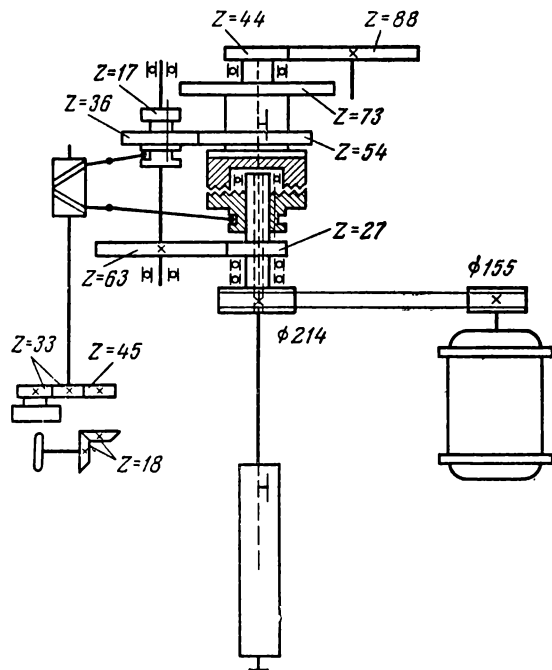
Кинематическая схема привода главного движения станка модели 2В440
